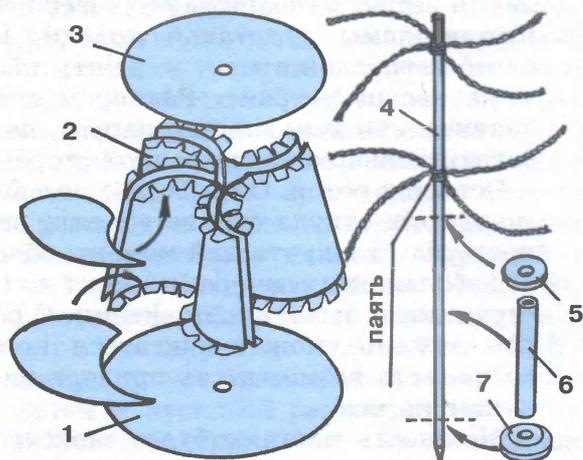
Конструкция ротора: 1 — верхний диск (картон); 2 — лопасти (ватман); 3 — нижний диск (картон); 4 — ось (сталь, латунь); 5 — шайба; 6 — резиновая трубка; 7 — шайба направляющая.
